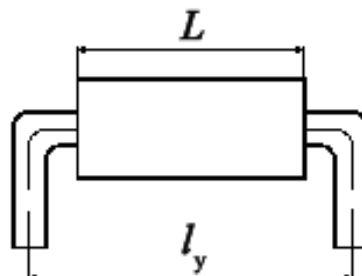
Обозначение установочного размера  $l_y$  для исполнений 1, 4–6, 14–16
